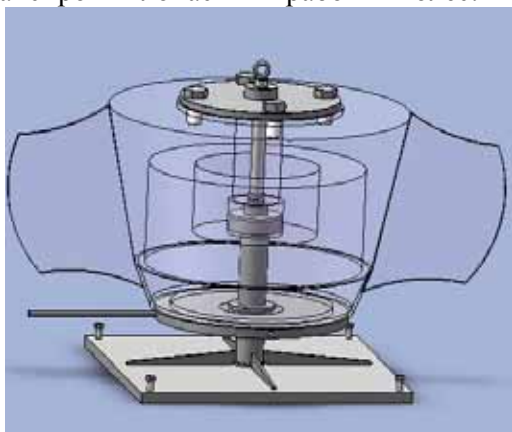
Установка осевого рабочего колеса насоса ОПВ 10–185 и центробежного рабочего колеса насоса СДВ 4000/28 на универсальный стенд для статической балансировки лопастных рабочих колёс
